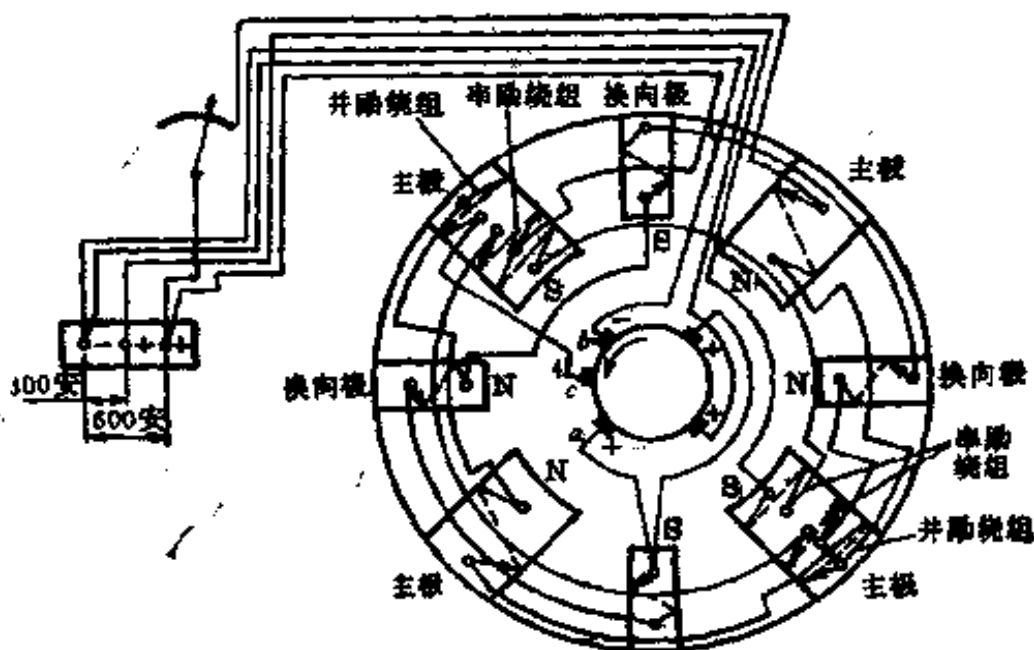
AX1-500 型(差复励式)直流弧焊发电机接线图
